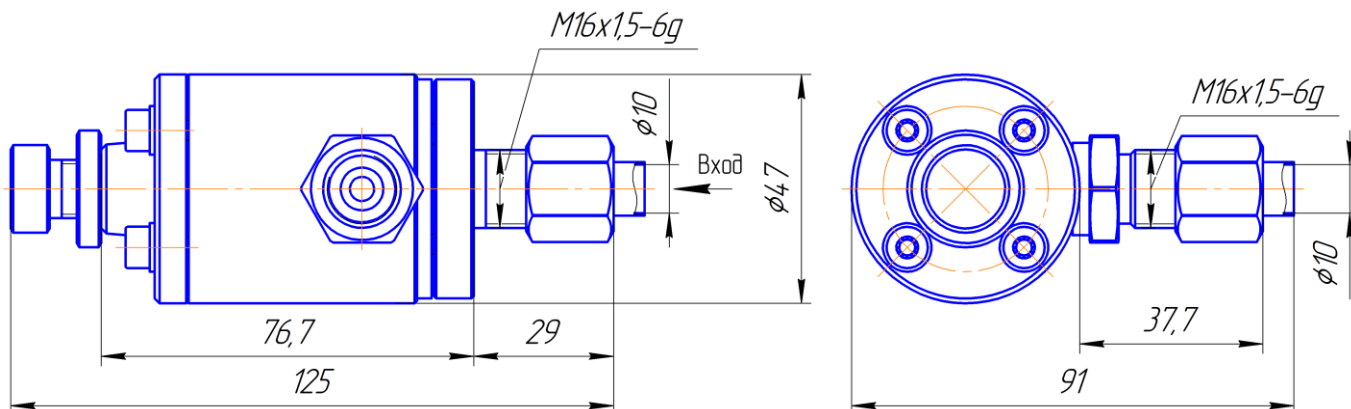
Габаритные и присоединительные размеры КЗС
